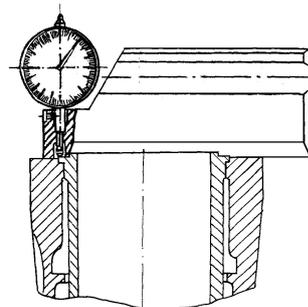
Приспособление И.806.01020 для проверки выступания гильзы над плоскостью блока цилиндров
